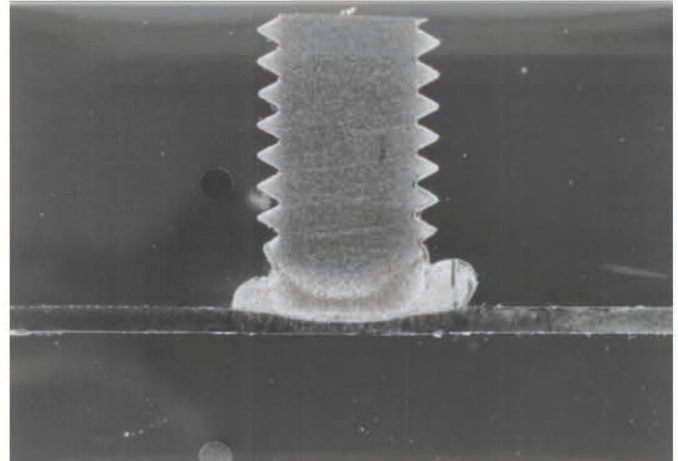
Schliffbild einer Kurzzzeitbolzenschweißung auf verzinktem Blech unter Schutzgas
